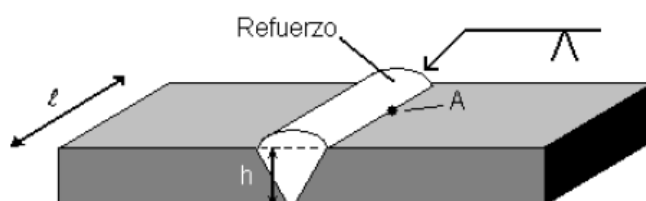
Sección transversal de cordón de soldadura (researchgate.net).
